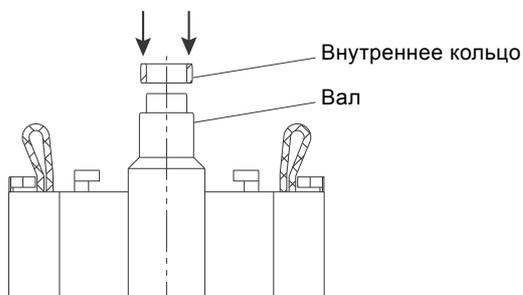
Сборка верхнего подшипника, KPL 1000-1800
